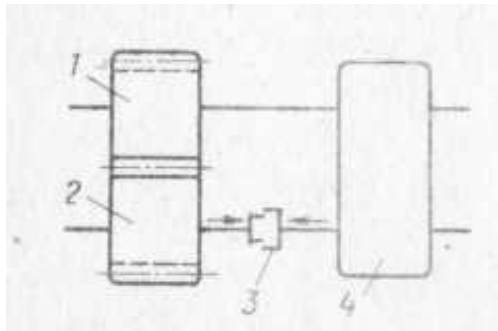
Принципова схема контролю кінематичної похибки зубчатого колеса
